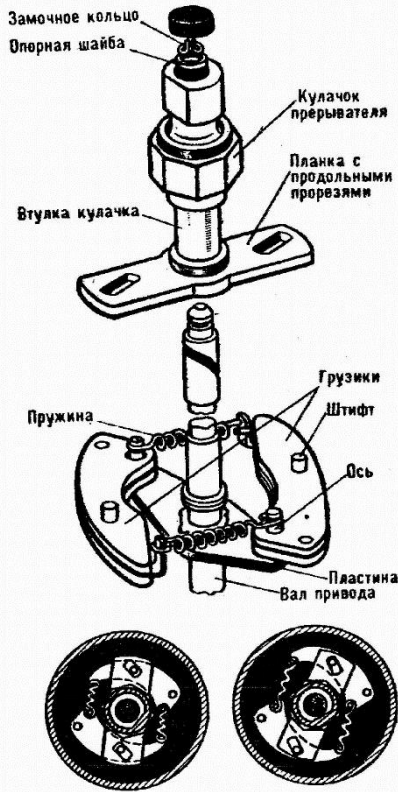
Центробежный регулятор опережения зажигания.
